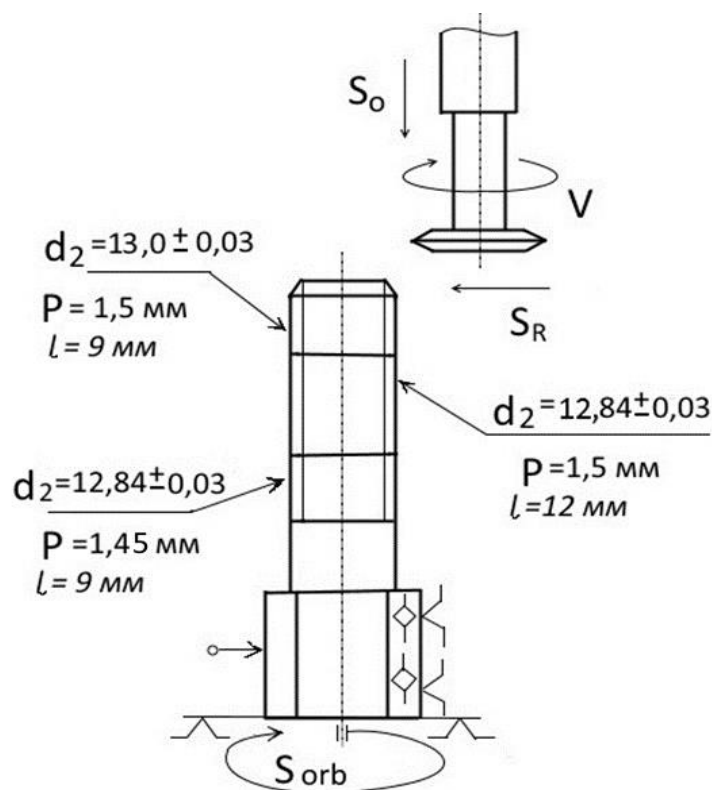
Схема обработки и размерные параметры исследуемого образца крепежной детали:
